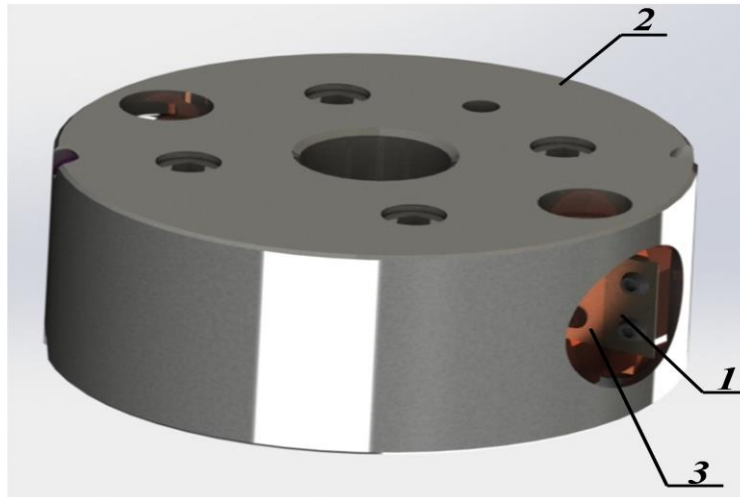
Фреза сборная с изменяемыми углами передним и наклона кромки
